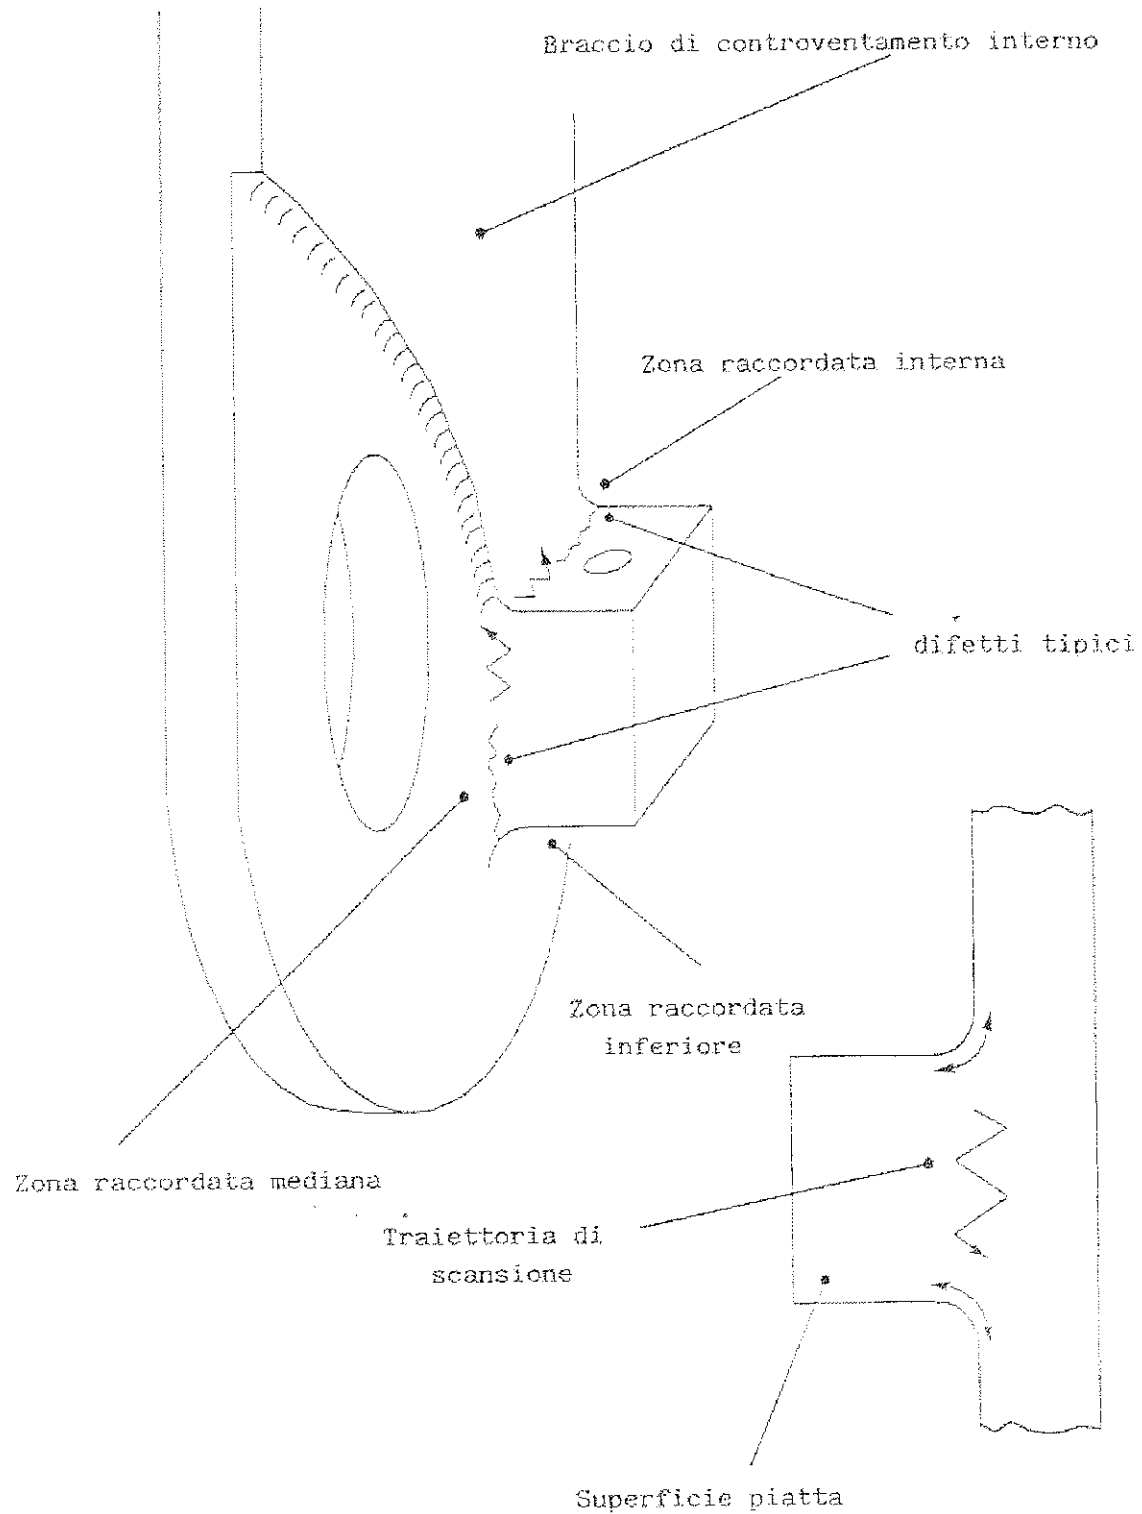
Spalla di bloccaggio in apertura del braccio di controventamento MLG : zone da esaminare
